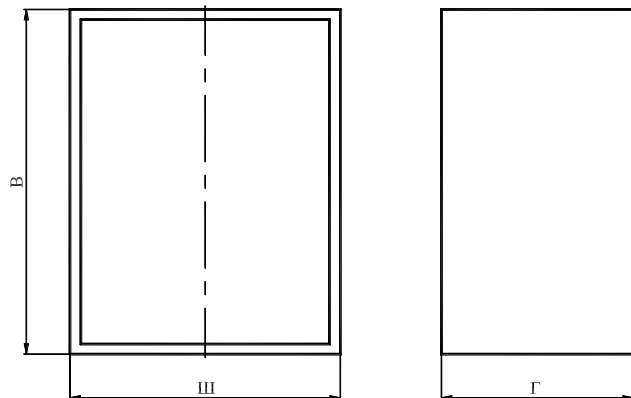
Габаритные размеры корпусов металлических ЩМП
